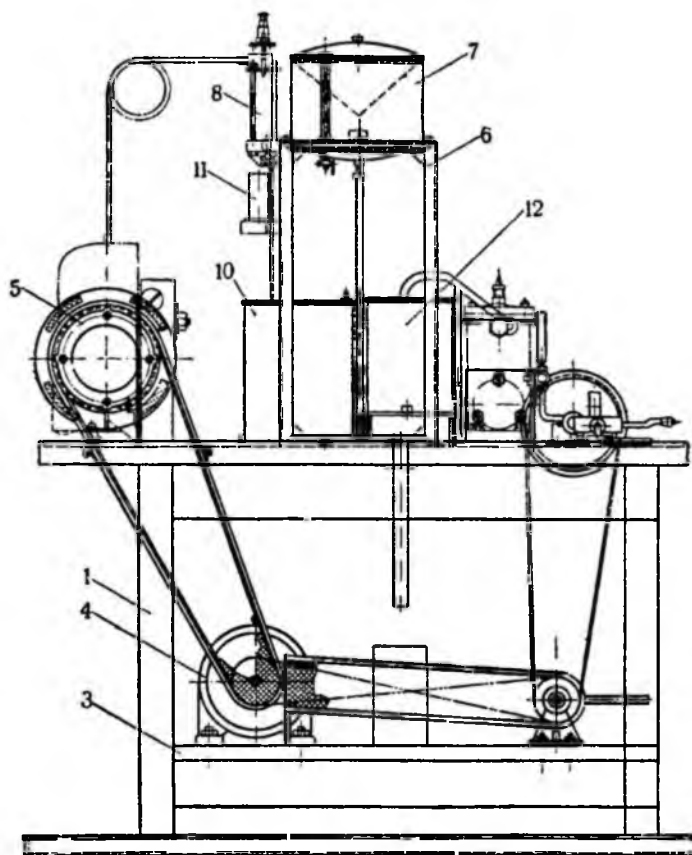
Универсальный стенд для испытания и регулировки насосов, подкачивающих помп и фильтров (вид спереди и сбоку). Выпуск 1938 г.
